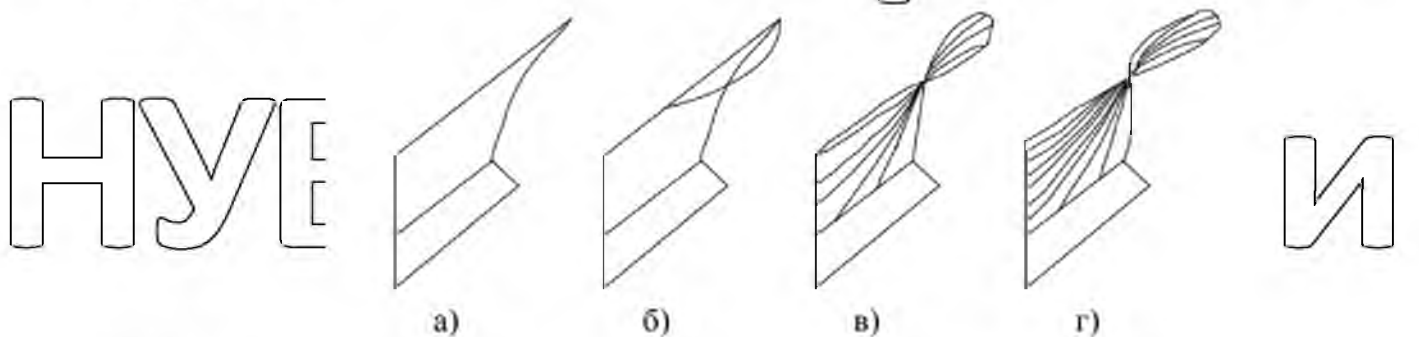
Схеми форм робочих поверхонь полиць: а - циліндрична; б - культурна; в - напівгвинтова; г - гвинтова
